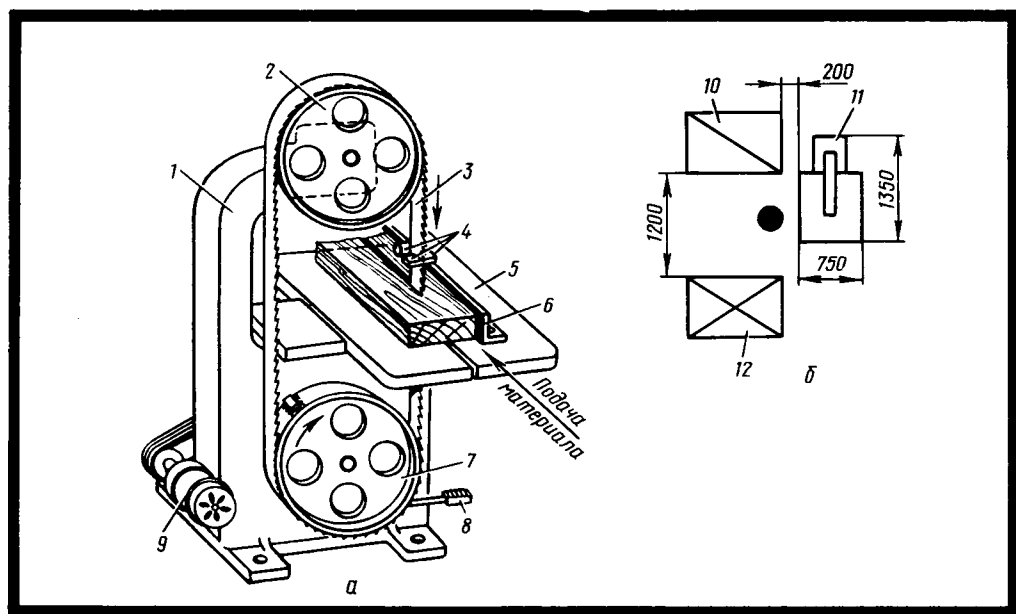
Станок ленточнопильный столярный ЛС80-5:
